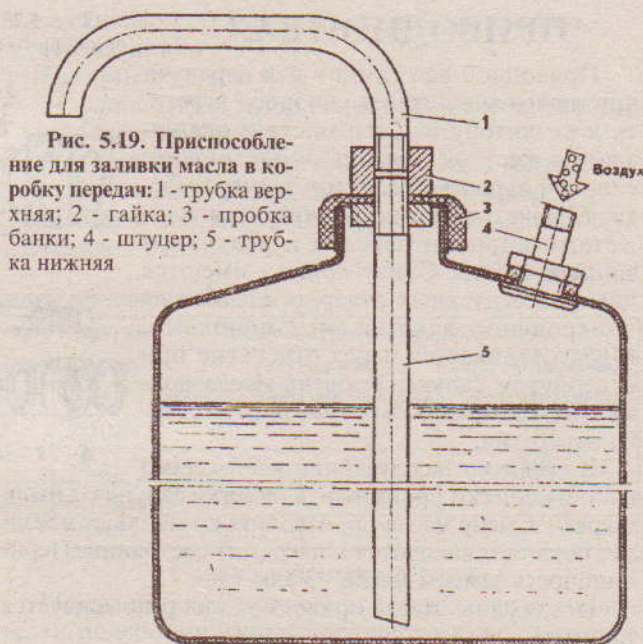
Приспособление для заливки масла в коробку передач: 1 - трубка верхняя; 2 - гайка; 3 - пробка банки; 4 - штуцер; 5 - трубка нижняя
